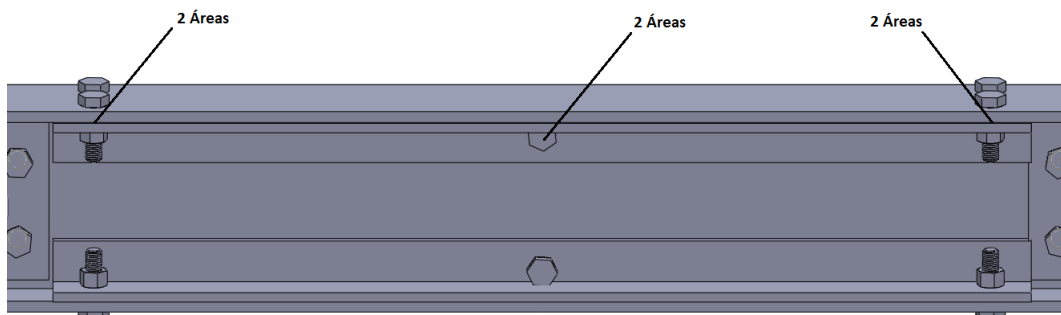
Disposição dos parafusos para o primeiro e ultimo ¼ do comprimento das vigas horizontais.
